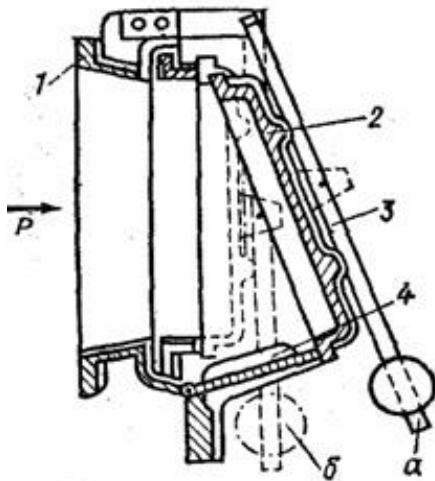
Предохранительный клапан с шарнирно-откидной дверцей:
